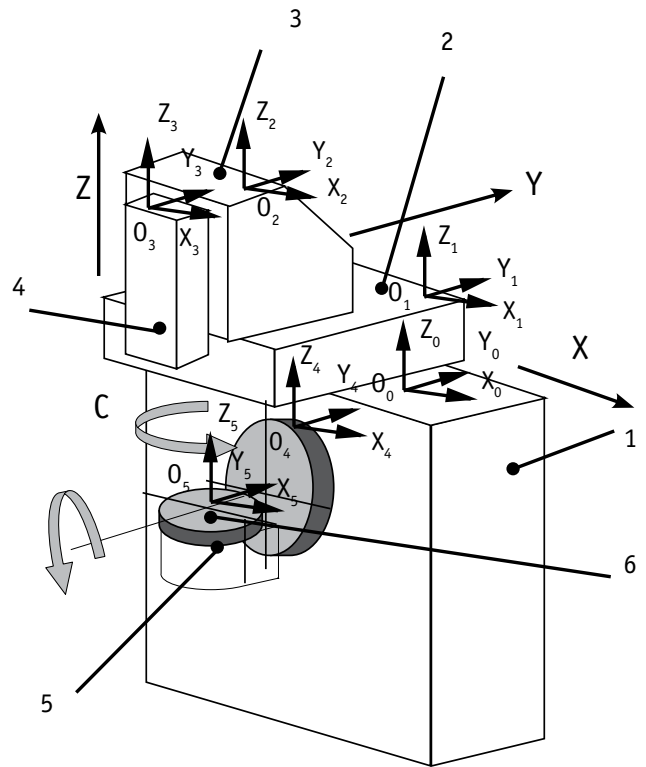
Схема соединения подсистем несущей системы станка: 1 – станина, 2 – салазки, 3 – стойка, 4 – шпиндельная бабка, 5 – корпус планшайбы, 6 – планшайба
